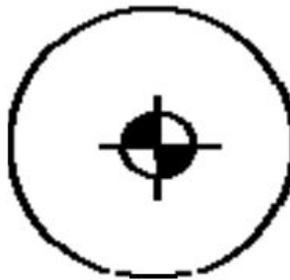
Вершина режущей кромки инструмента в начальной точке
